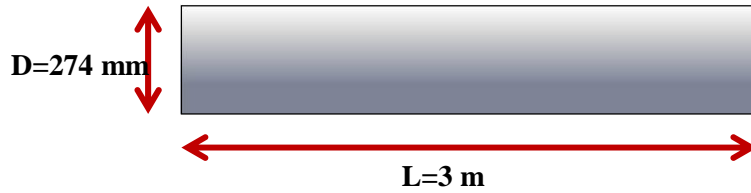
Dimensiones del Rodillo. Fuente (Propia)
